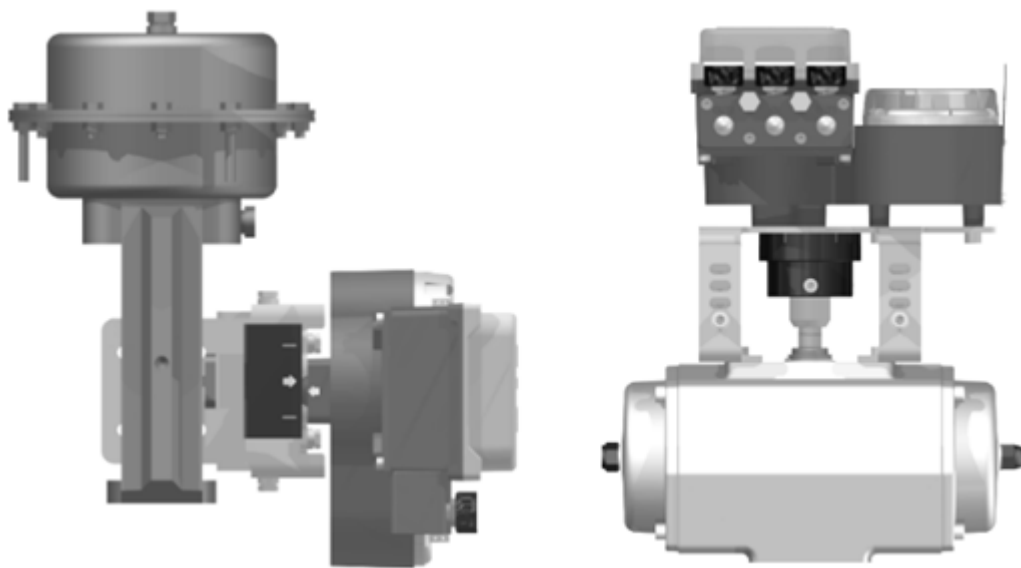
Montaje del VVP10 en actuadores de válvulas con imanes lineal y giratorio.
